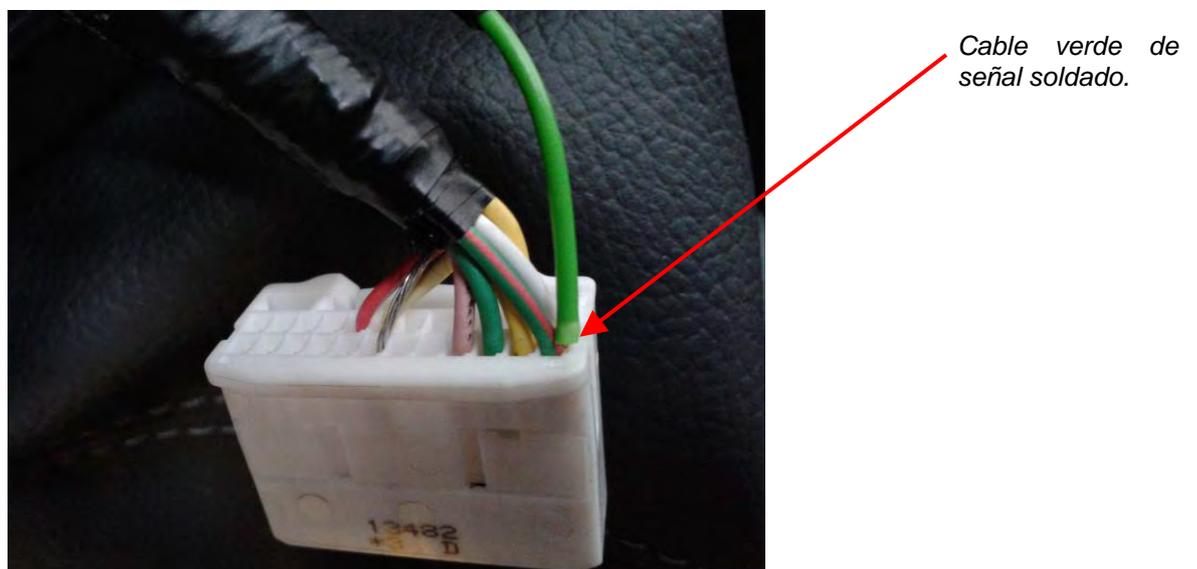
Vista del conector con el cable verde de señal soldado.
